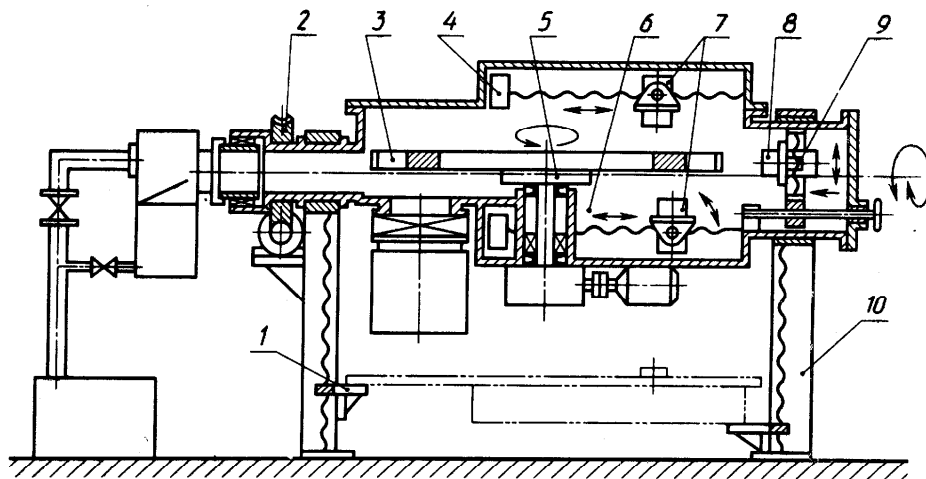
Схема установки с поворотной камерой для электронно-лучевой сварки пакетов лопаток
